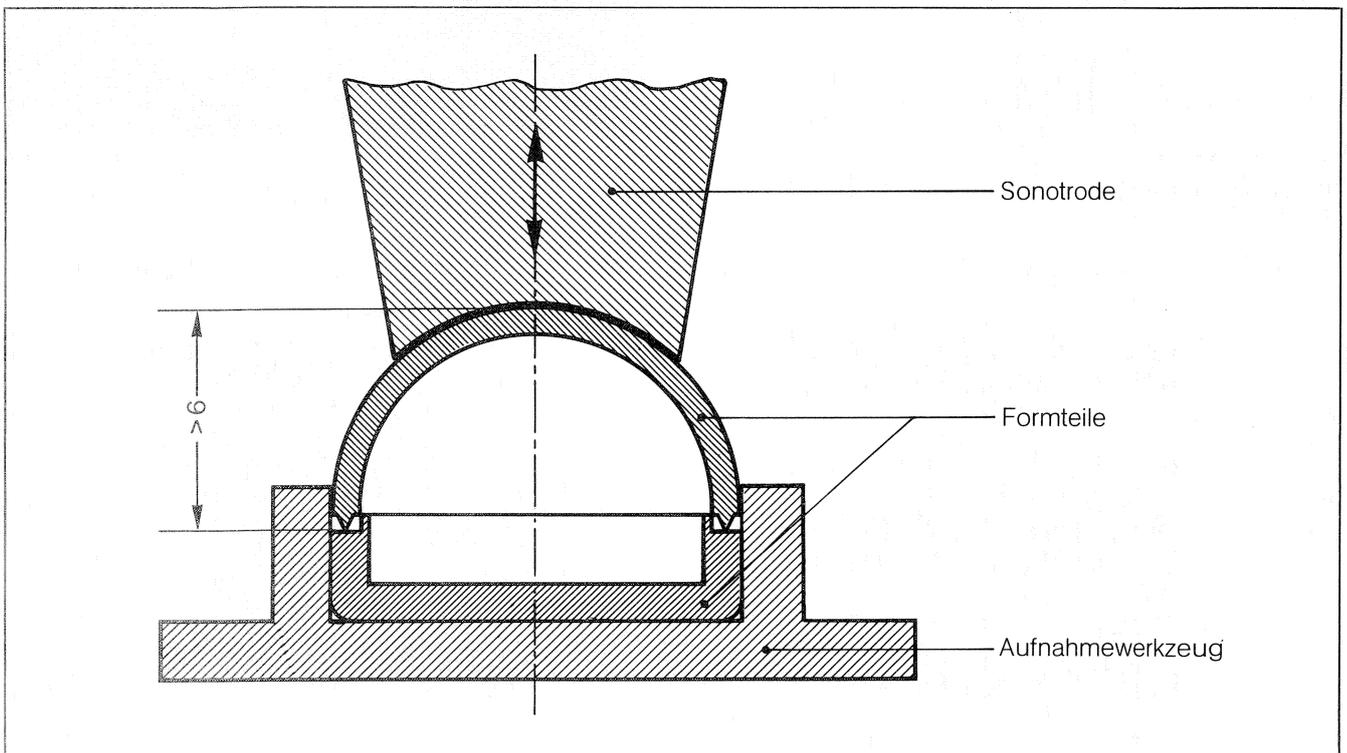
Ultraschallschweißen im Fernfeld
